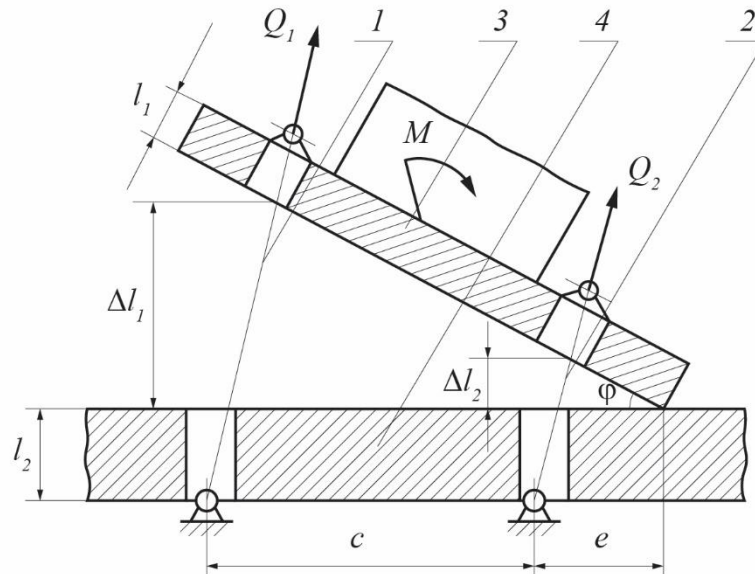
Розрахункова схема вузла кріплення вентилятора
